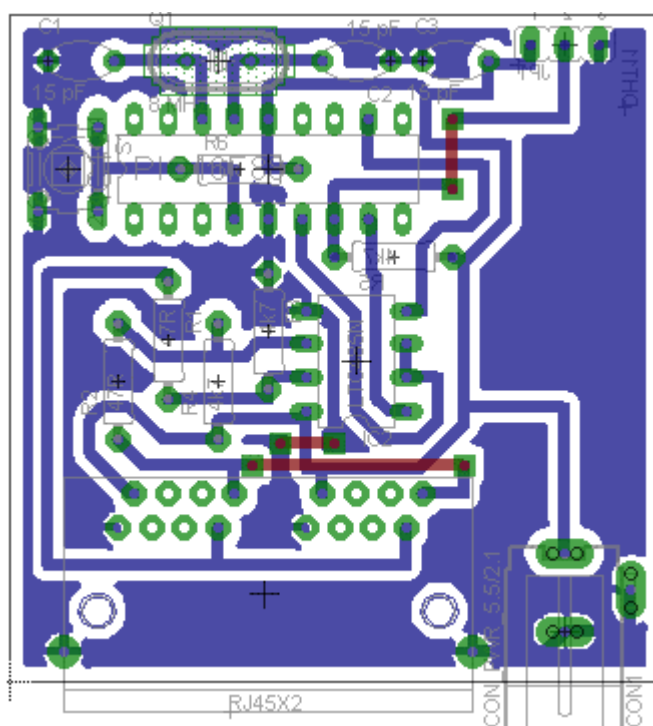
Návrh PCB ovládacího panelu – strana součástek
